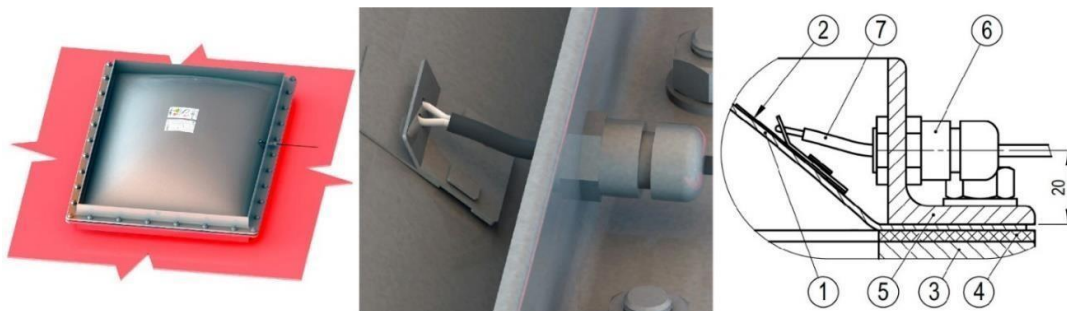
Установка кабеля индикатора G1 в проход в L-образный профиль
